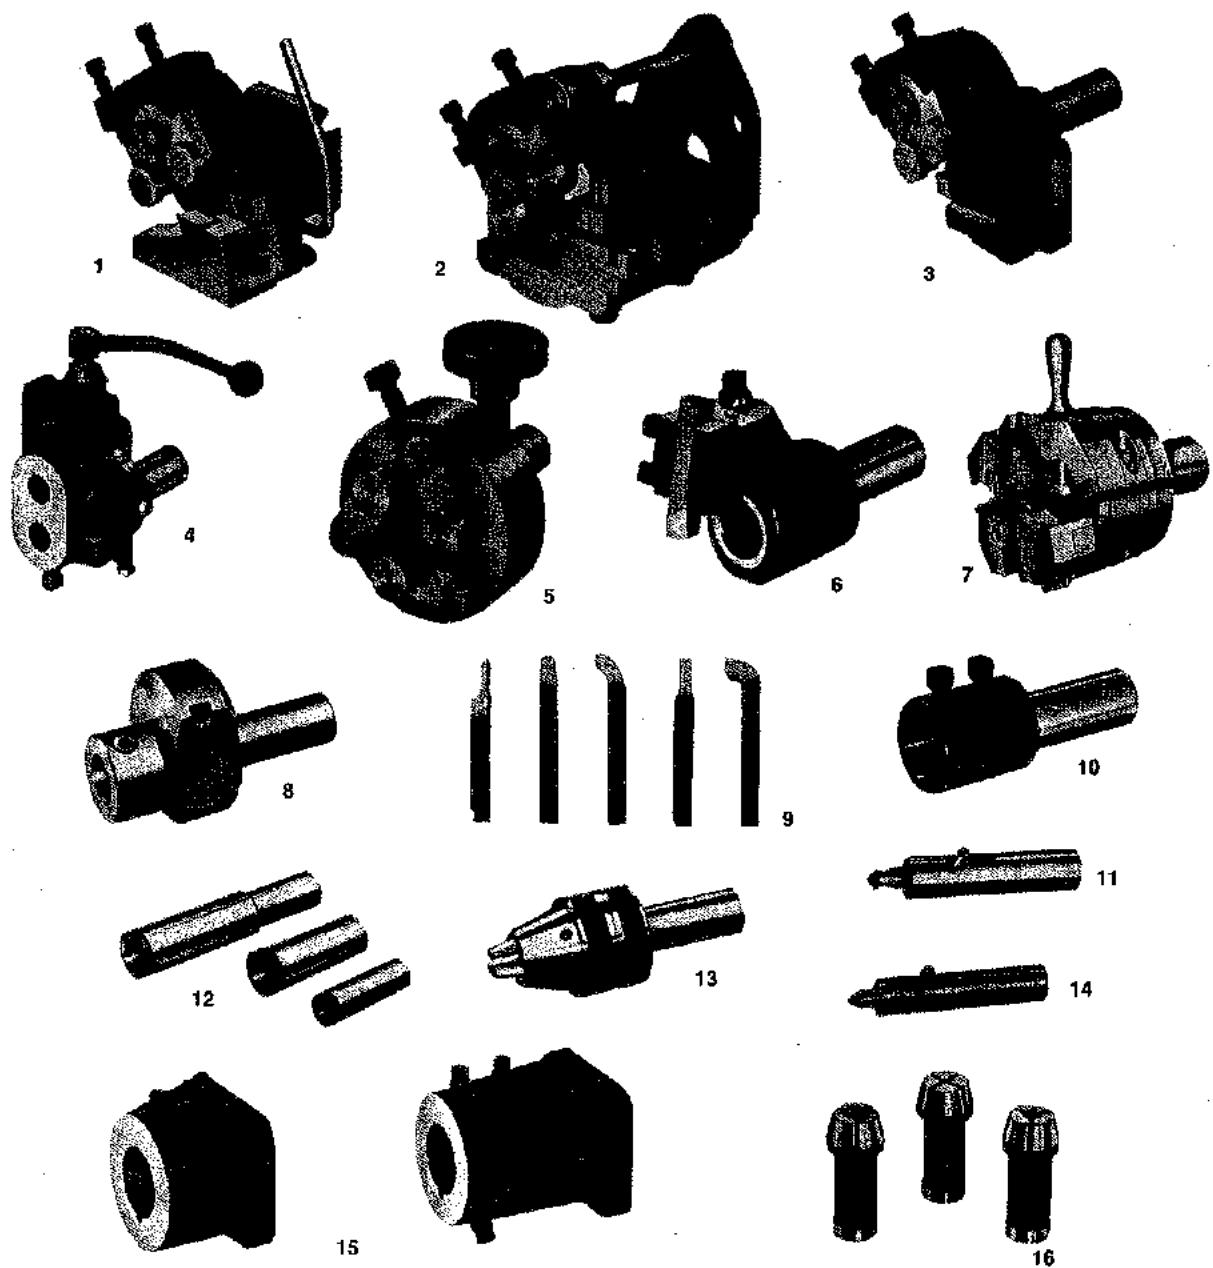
Equipo de herramientas universal para trabajos sobre barra (Warner & Swasey Co. y Landis Machine Co.)
